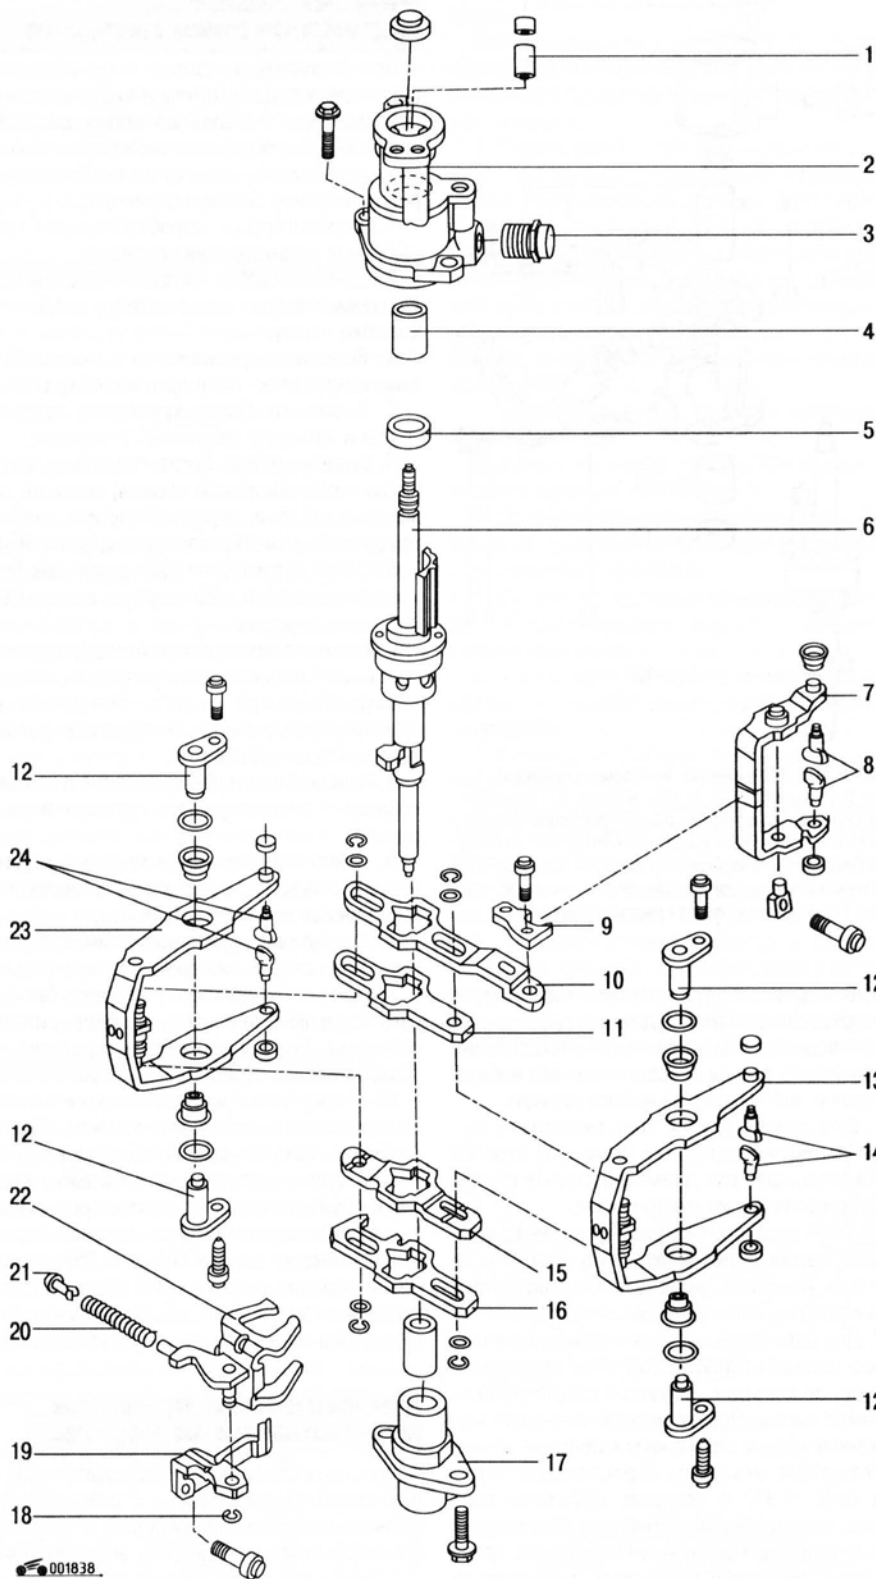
Механизм переключения передач: 1 – втулка; 2 – корпус; 3 – стопорный винт; 4 – опорная втулка; 5 – уплотнительное кольцо; 6 – вал механизма выбора передач; 7 – вилка включения V передачи; 8 – наконечник вилки включения V передачи; 9 – рычаг включения V передачи; 10 – рычаг вилки включения V передачи; 11 – рычаг вилки включения III и IV передач; 12 – цапфа вилки включения передач; 13 – вилка включения III и IV передач; 14 – наконечник вилки включения III и IV передач; 15 – рычаг вилки включения I и II передач; 16 – рычаг вилки включения передачи заднего хода; 17 – опора вала; 18 – стопорное кольцо; 19 – держатель вилки включения передачи заднего хода; 20 – пружина; 21 – штифт; 22 – вилка передачи заднего хода; 23 – вилка включения I и II передач; 24 – наконечник вилки включения I и II передач
